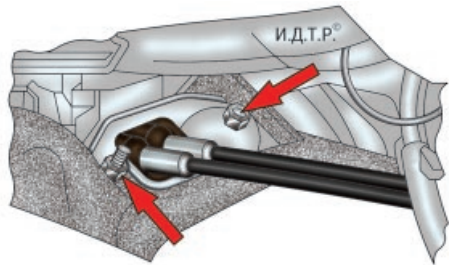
Крепление уплотнителя тросов управления коробкой передач
